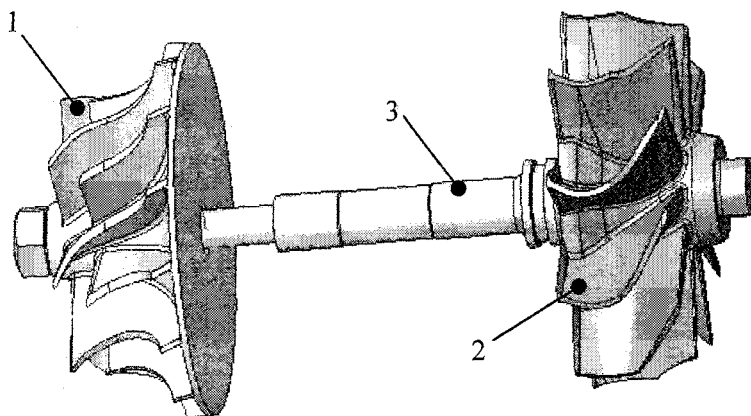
Твердотельные модели элементов ротора: 1 – компрессорное колесо; 2 – турбинное колесо; 3 – вал ротора
